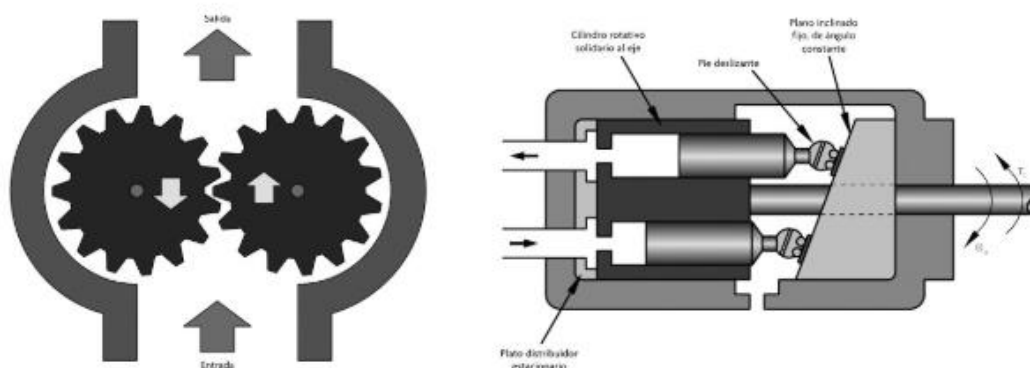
Motor hidráulico con engranes (1) motor hidráulico de pistones axiales(2).
